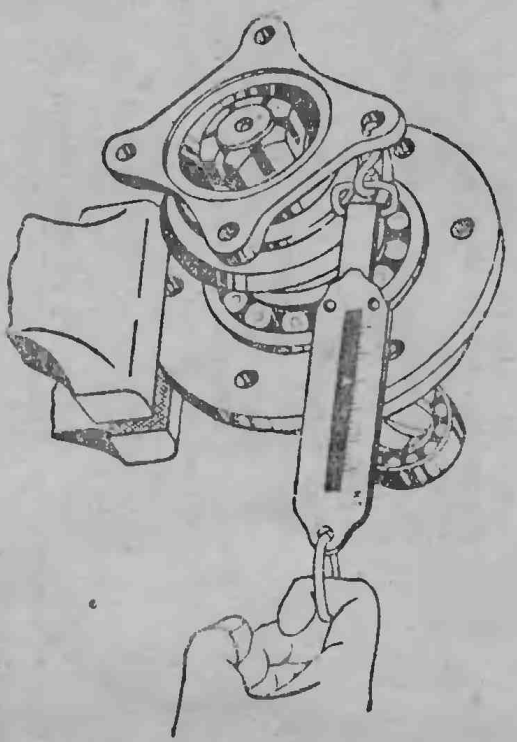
Проверка затяжки подшипников ведущей шестерни
